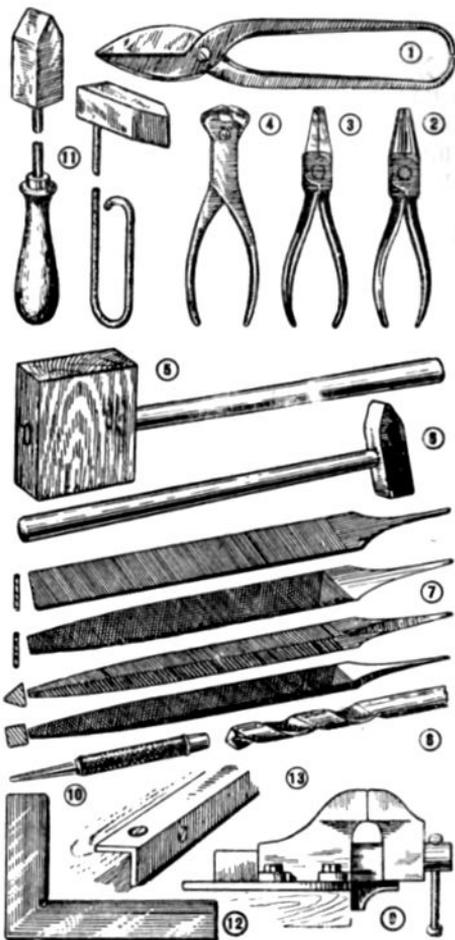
Инструменты и приспособления для работы с проволокой и жестью:
